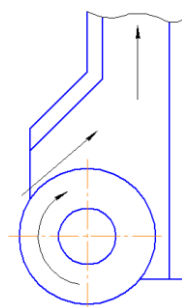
Устройство местной вентиляции для полировальной бабки.
